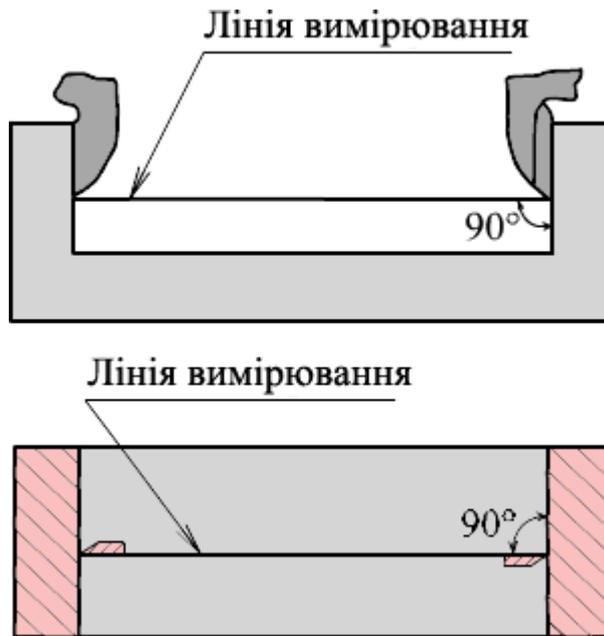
Положення губок внутрішніх паралельних поверхонь
